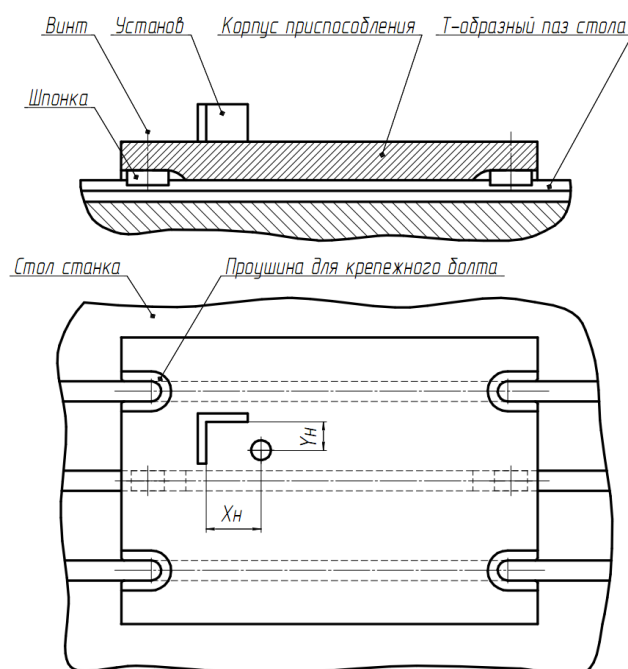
Базирование приспособления на столе станка по шпонкам и продольному пазу
